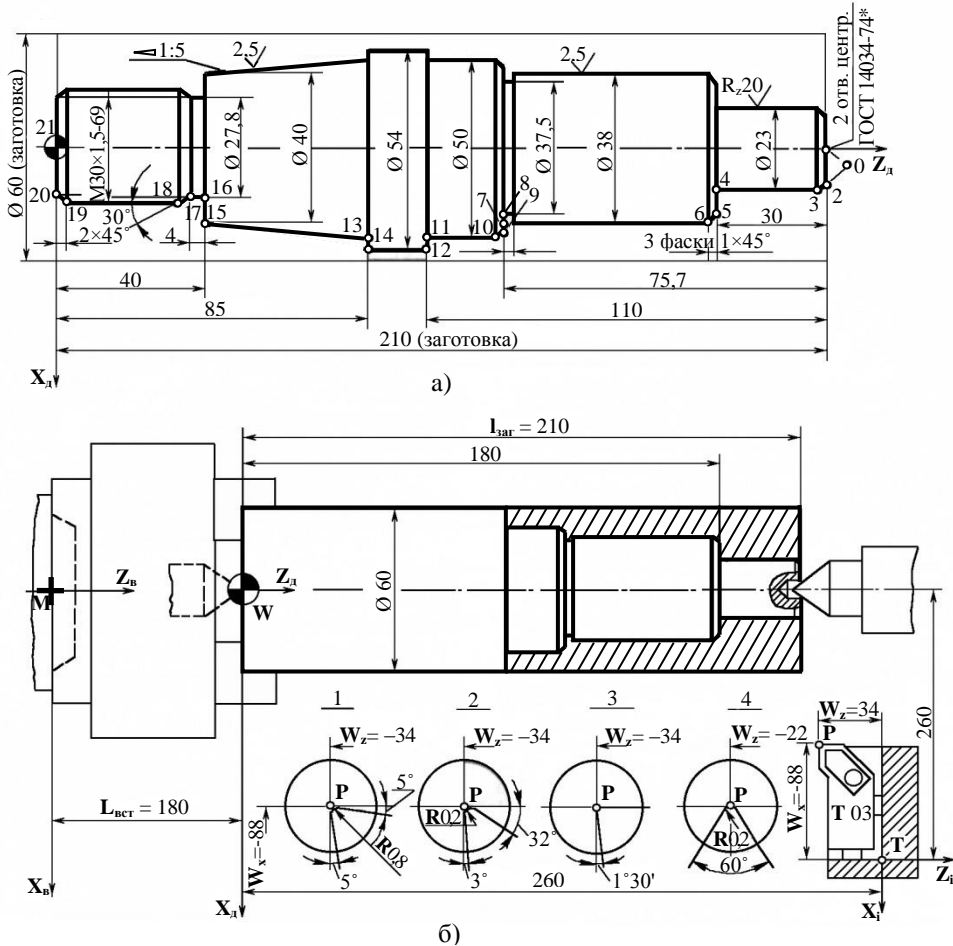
Обробка деталі “вал” на токарному верстаті:
